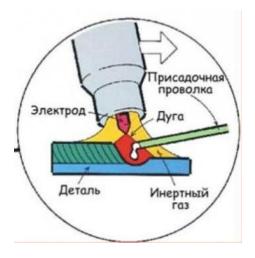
Аргонодуговая сварка с присадочной проволокой
